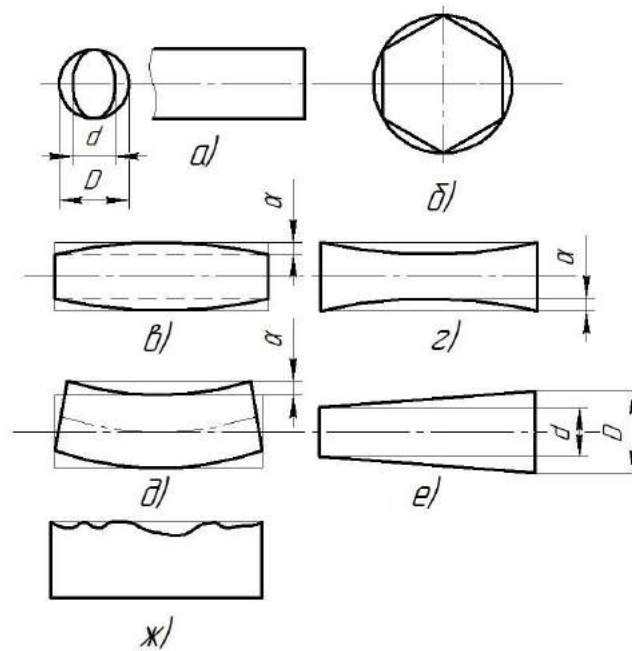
Похибки форми поверхонь при обробленні на важких токарних верстатах
